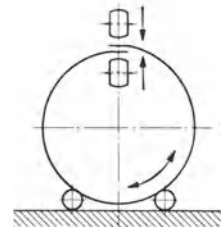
Grundform der Druckrollen-Wassergasschweißung.
